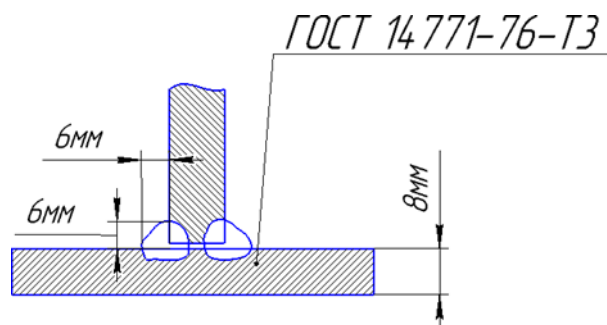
Сварной шов приварки окрайки к стенке резервуара
